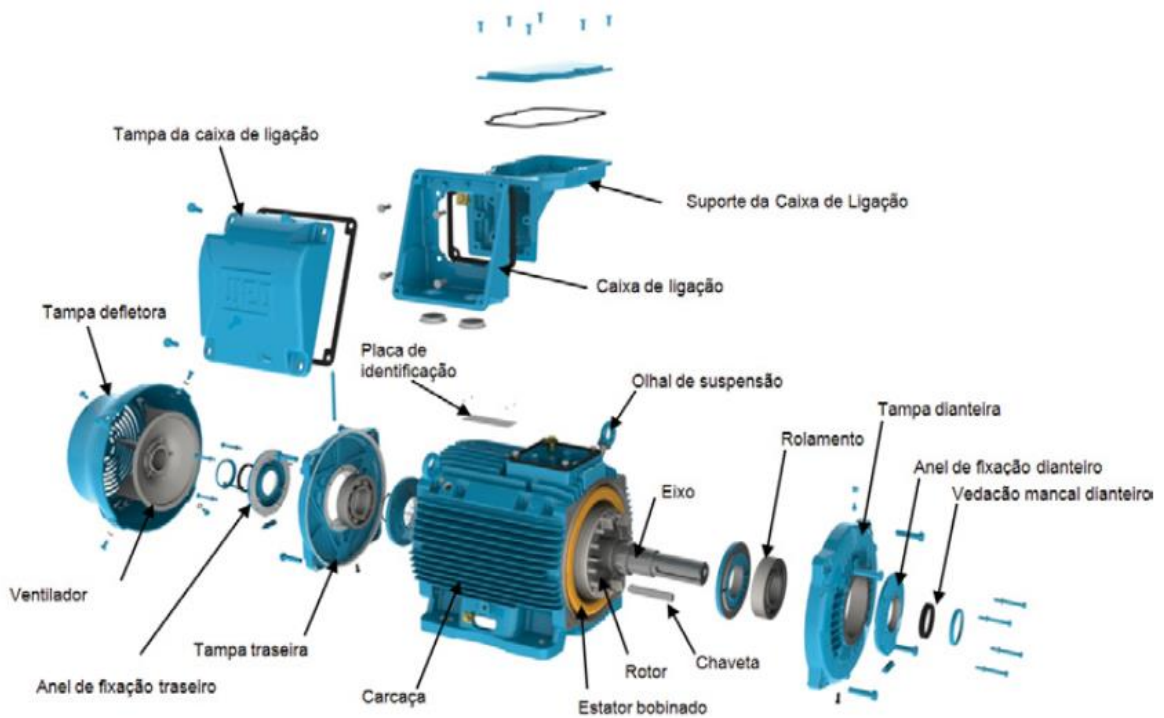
Vista explodida de um motor de indução Fonte: Weg (2016).
